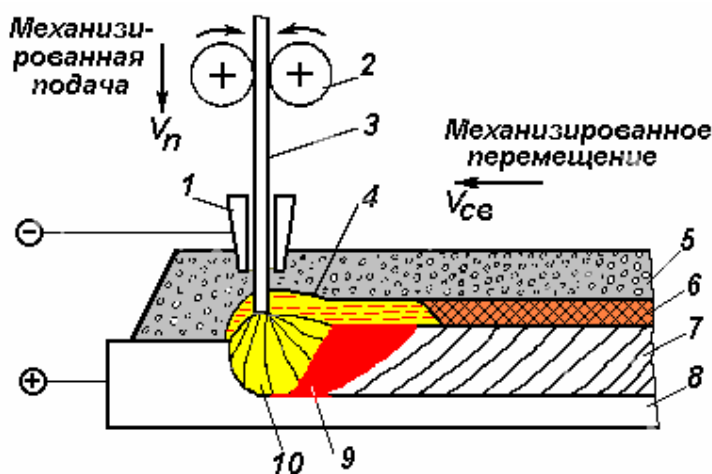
Схема процесса автоматической дуговой сварки под флюсом
